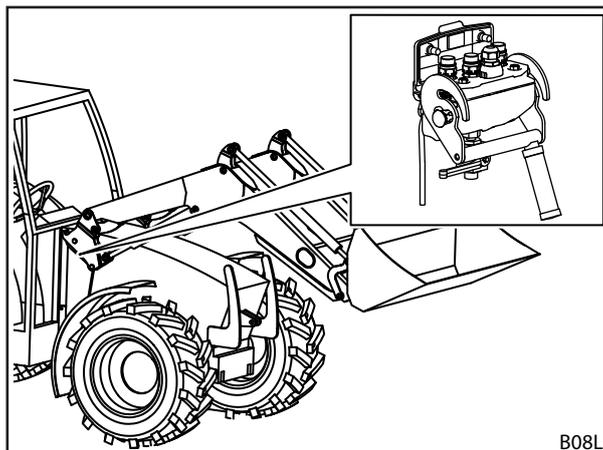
Hydro-Fix: posizione sul caricatore frontale
